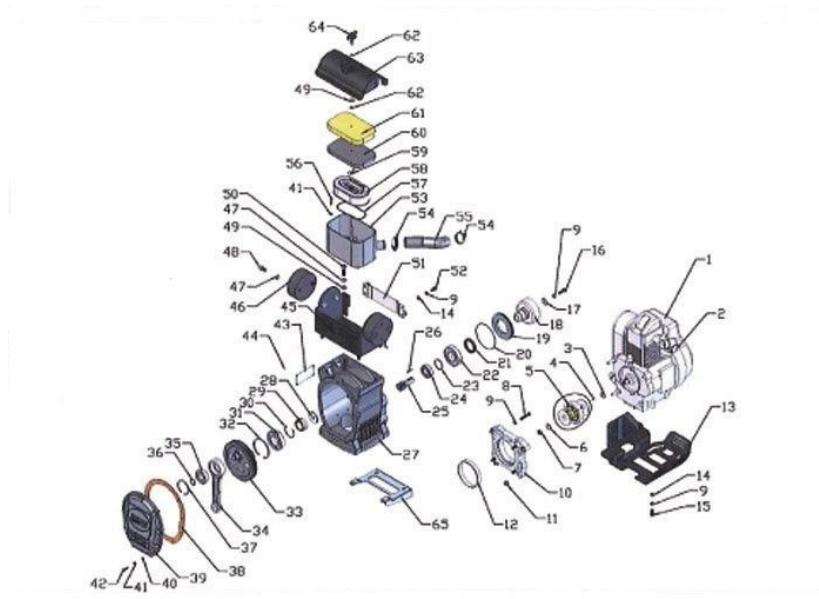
AY-68 H PV — Figura 2: motor, cárter e transmissão
